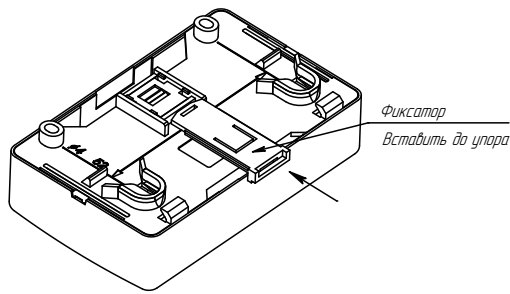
Установка фиксатора для крепления на DIN-рейку
